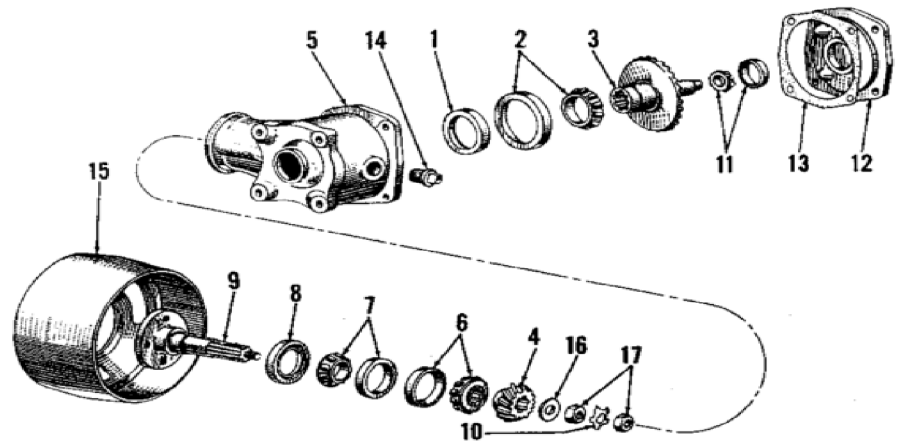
Exploded view of riem katrol assemblage beschikbaar voor de modellen 2000 en 3000.
